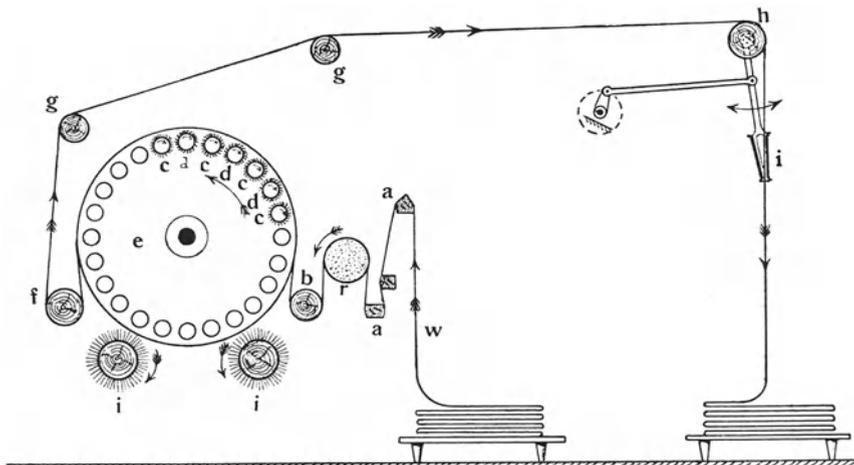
Universal-Kratzenrauhmaschine von Geßner.
